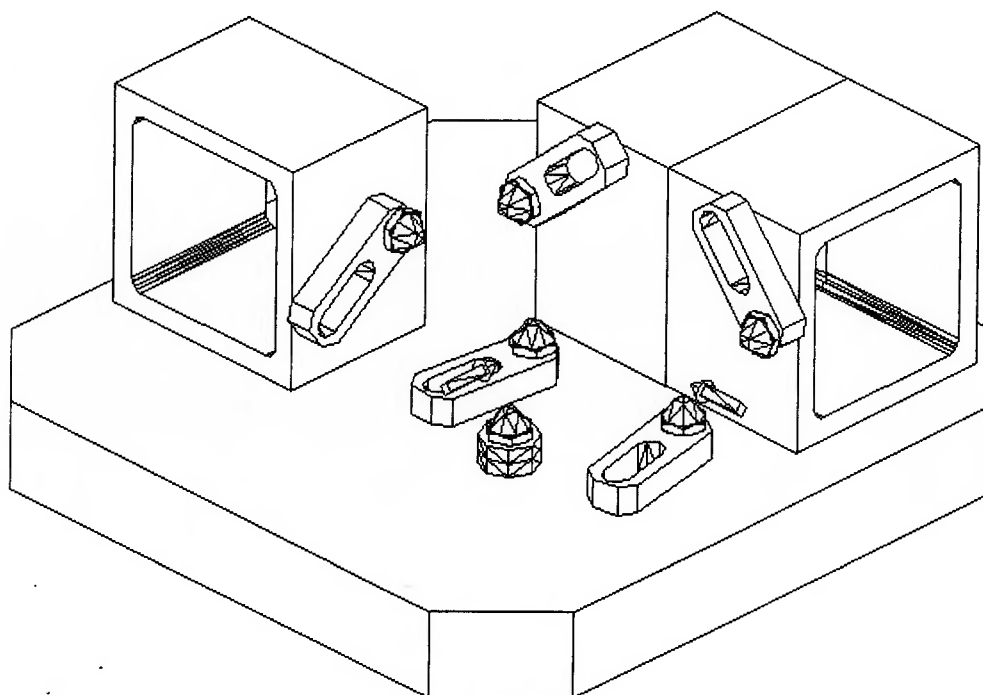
Montagem do dispositivo para usinagem de F13 ; F15 ; F4 ; F8 ;
